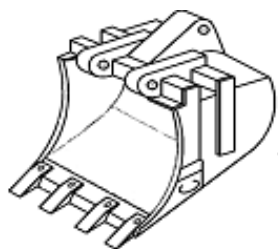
Ковшовый рабочий орган с днищем в виде гладкой поверхности
